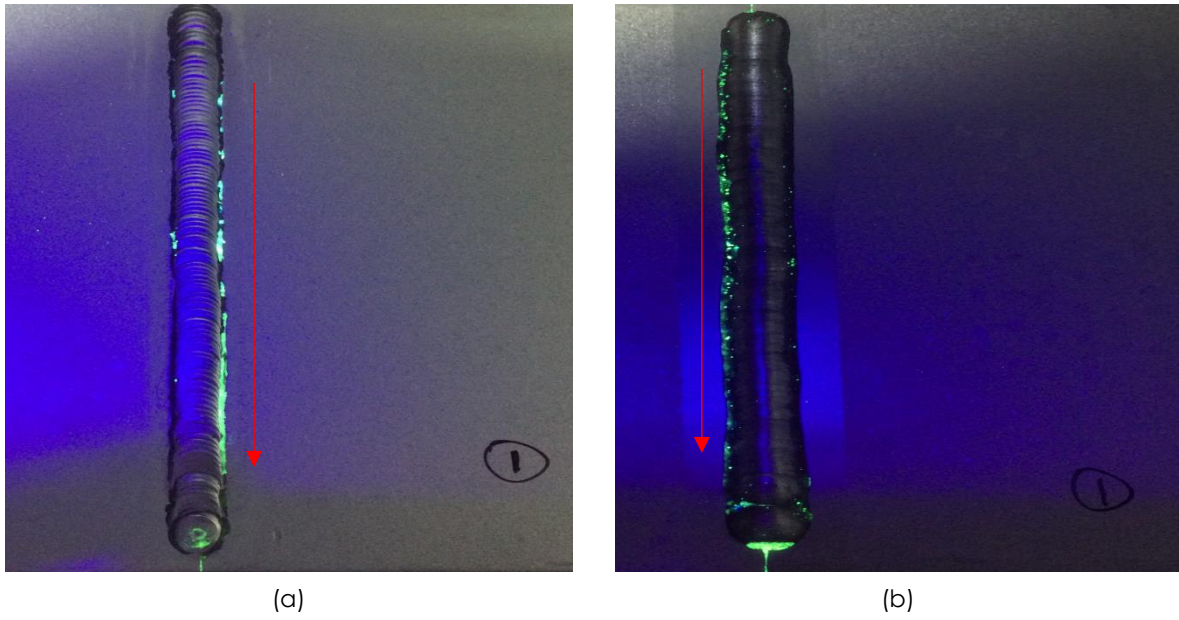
(a) Cordón Soldadura Superior Probeta 1. (b) Cordón de Soldadura Inferior Probeta 1.
